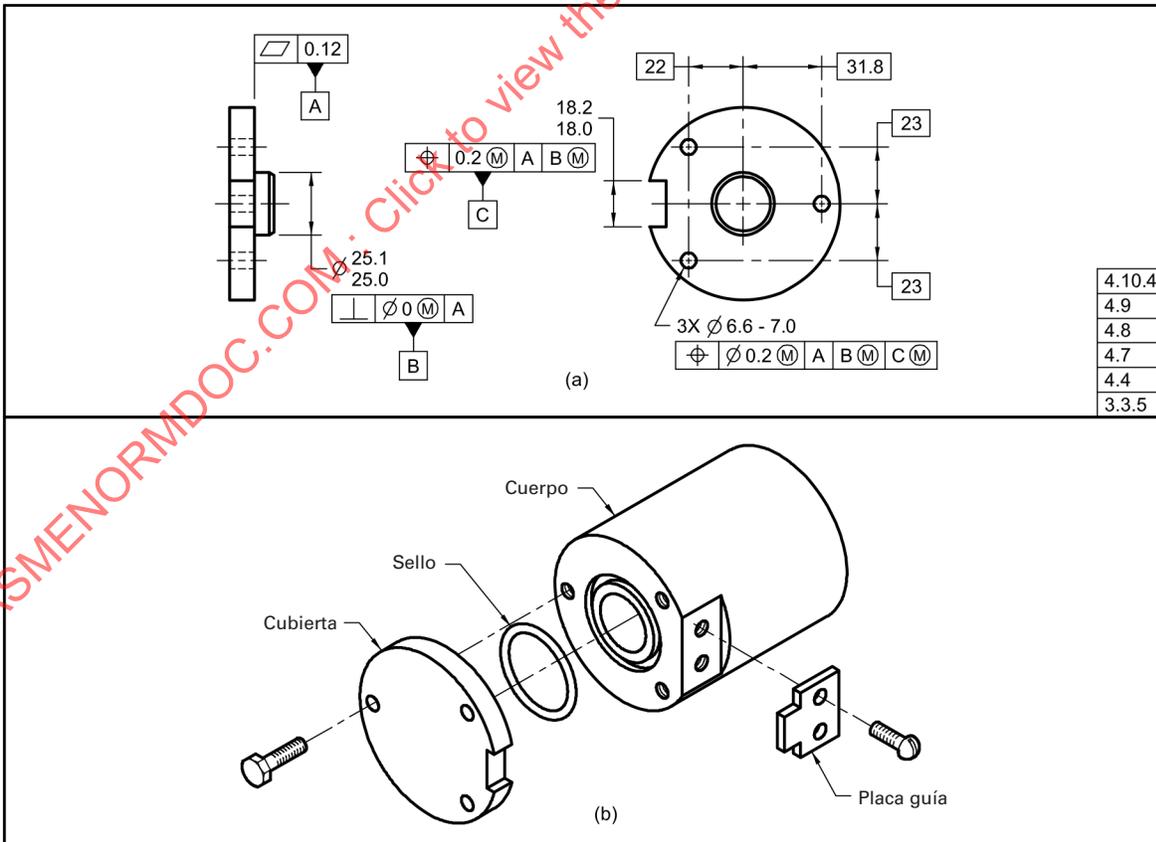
Desarrollo de un Marco de Referencia Datum para la Pieza en la Fig. 4-5
